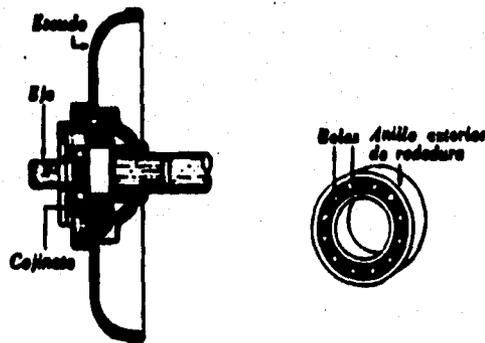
Cojinete de bolas. A la derecha, suelto; a la izquierda, montado en un escudo.
